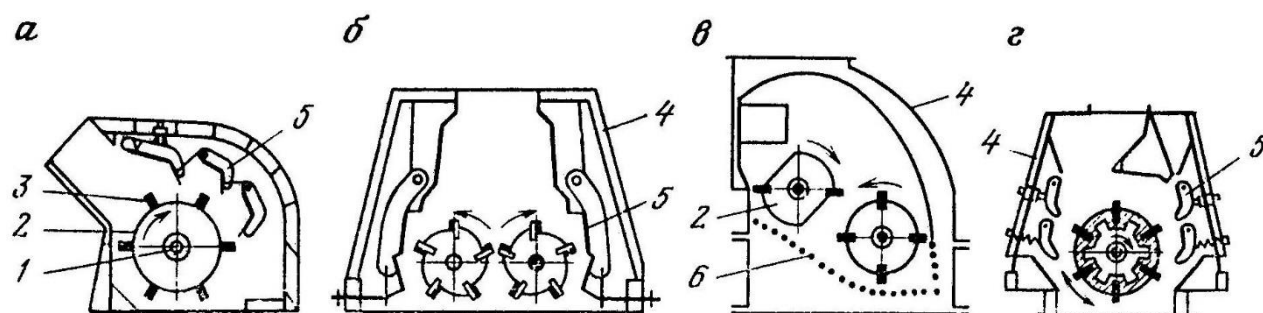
Основні схеми роторних дробарок [16, 17, 21]: а - однороторна; б - двороторна паралельного дроблення; в - двороторна послідовного дроблення; г - однороторна реверсивна; 1 - горизонтальний вал; 2 - масивний ротор; 3 - била; 4 - корпус дробарки; 5 - відбійні плити; 6 - колосникова решітка
